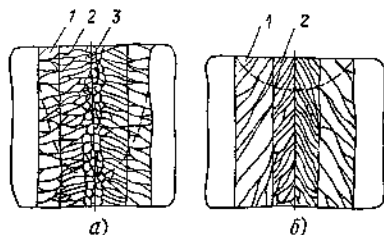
Строение металла шва при электрошлаковой сварке:
